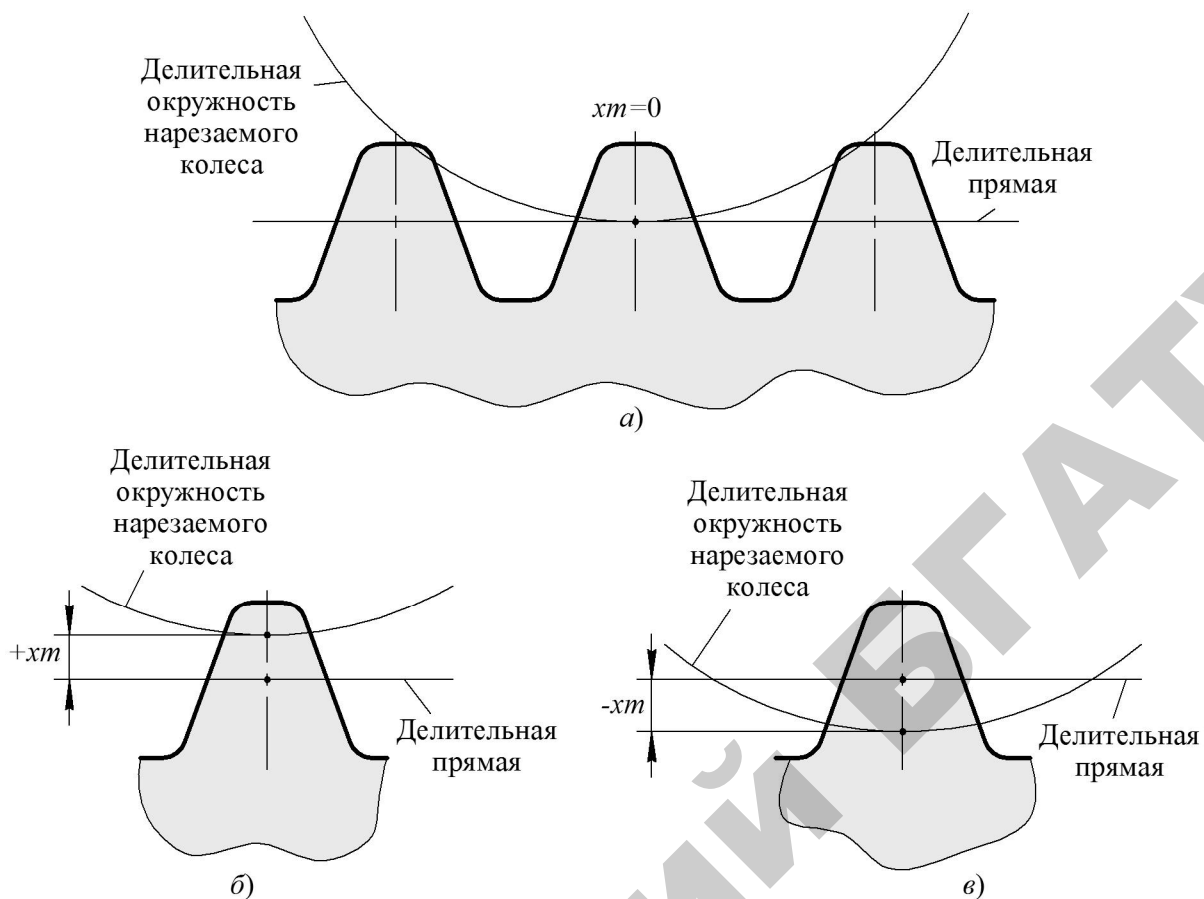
Способы расположения исходного производящего контура рейки режущего инструмента относительно изготавливаемого зубчатого колеса
